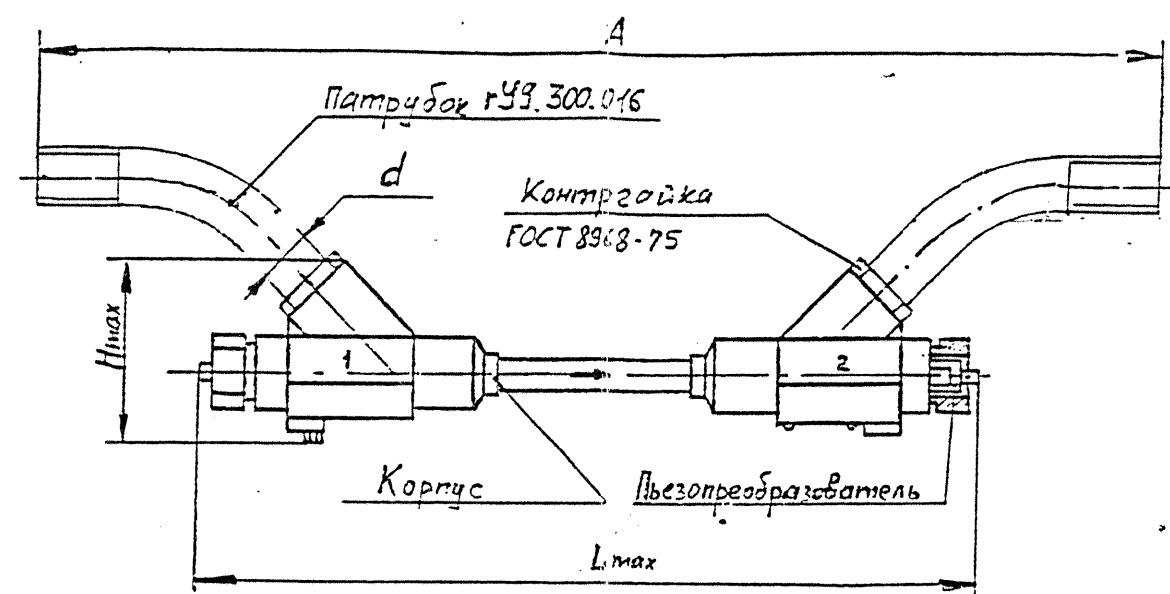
Преобразователь первичный ПП14М. Общий вид
